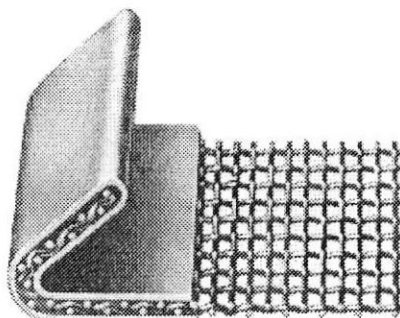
Gancho Tipo 2 con Platina Metálica.
